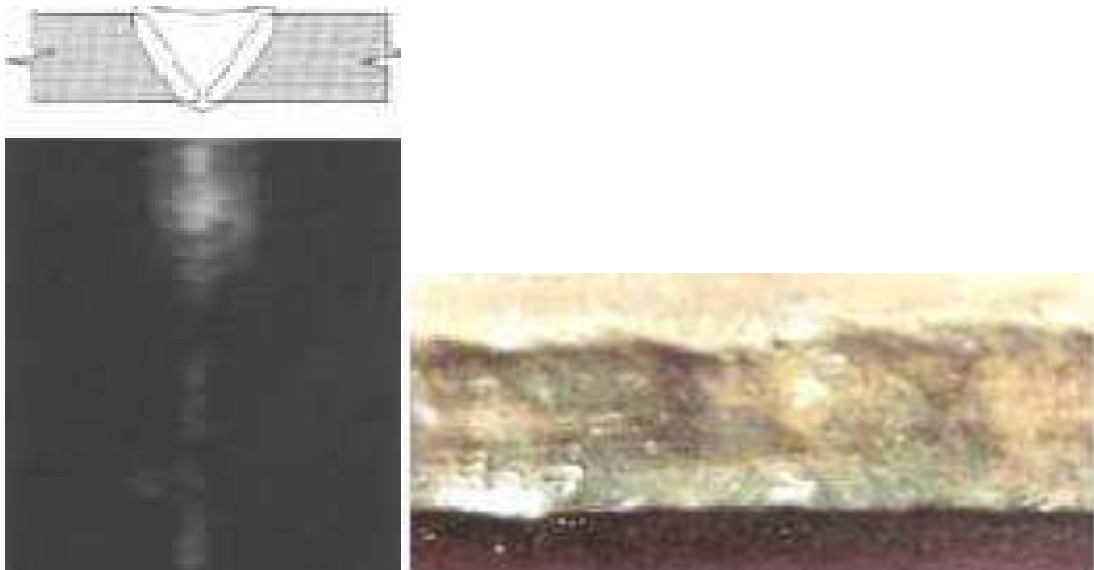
Junta soldada con concavidad externa.
